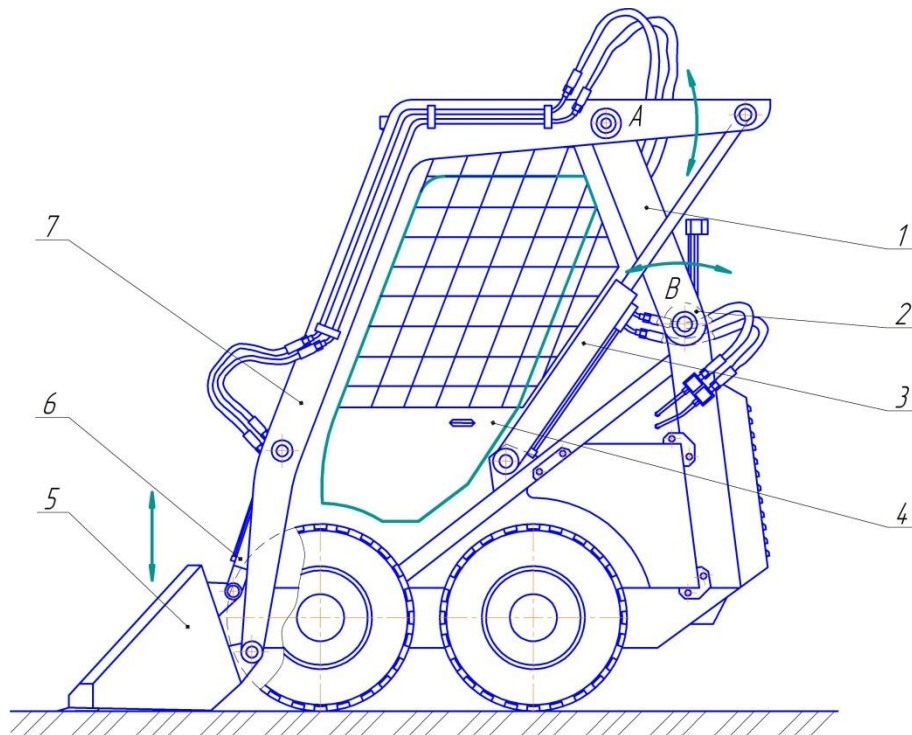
Конструкция УМП: 1 – рама; 2 – моментные гидроцилиндры; 3 – гидроцилиндры подъема-опускания стрелы; 4 – вход в кабину оператора; 5 – ковш; 6 – гидроцилиндр поворота ковша; 7 – стрела; А, В – шарниры; стрелками показано направление движения элементов конструкции относительно шарниров
